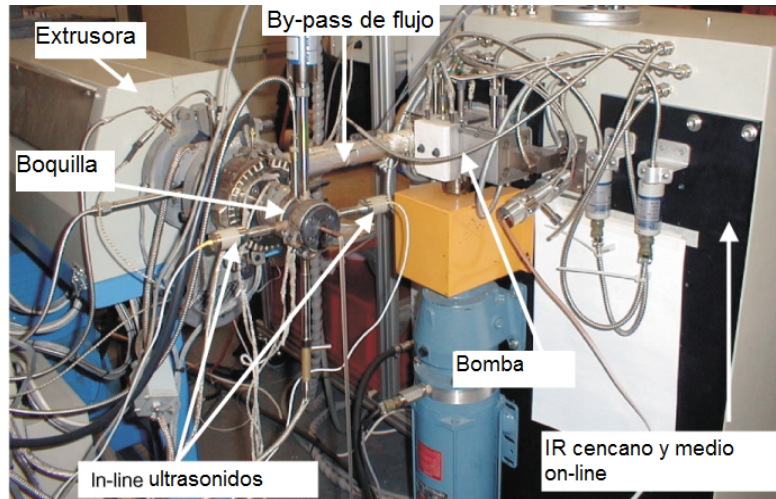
Montaje equipamiento de medidas on-line<sup>25</sup>.
